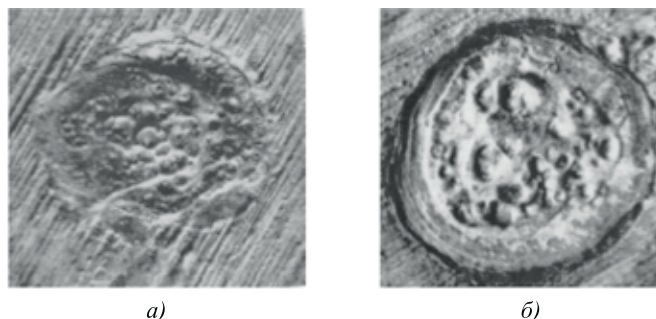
Отпечатки анодного (а) и катодного (б) пятен сварочной дуги на поверхности металла [89]
